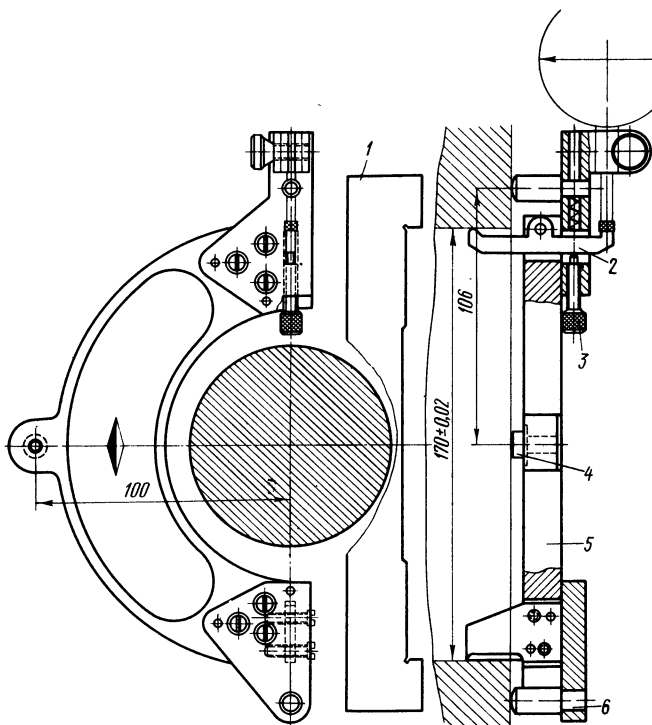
Штихмасс с индикатором для проверки отверстий без съема борштанги
